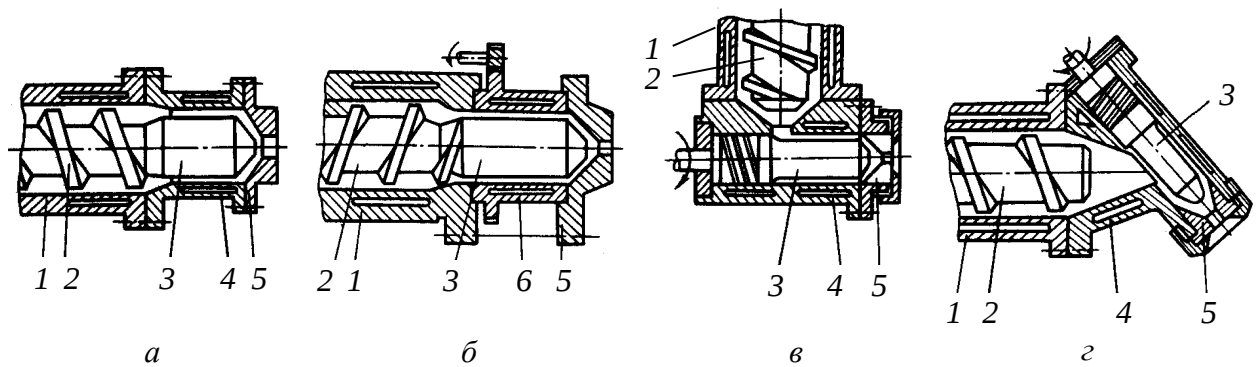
Схеми змішувальних елементів без регулювання (а) і з регулюванням (б–г) відносної швидкості обертання їхніх робочих поверхонь [33]: 1 – циліндр; 2 – черв'як; 3 – дорн; 4 – корпус головки; 5 – формувальний інструмент; 6 – обертова втулка
